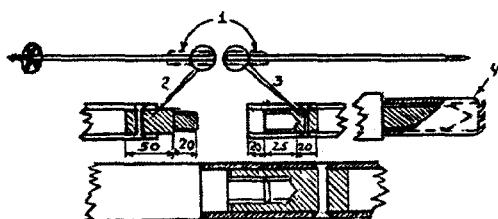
Лавинный щуп из лыжных палок: 1 — снимаемые рукоятки; 2 — болт; 3 — втулка с нарезкой; 4 — насадка на штычок палки
